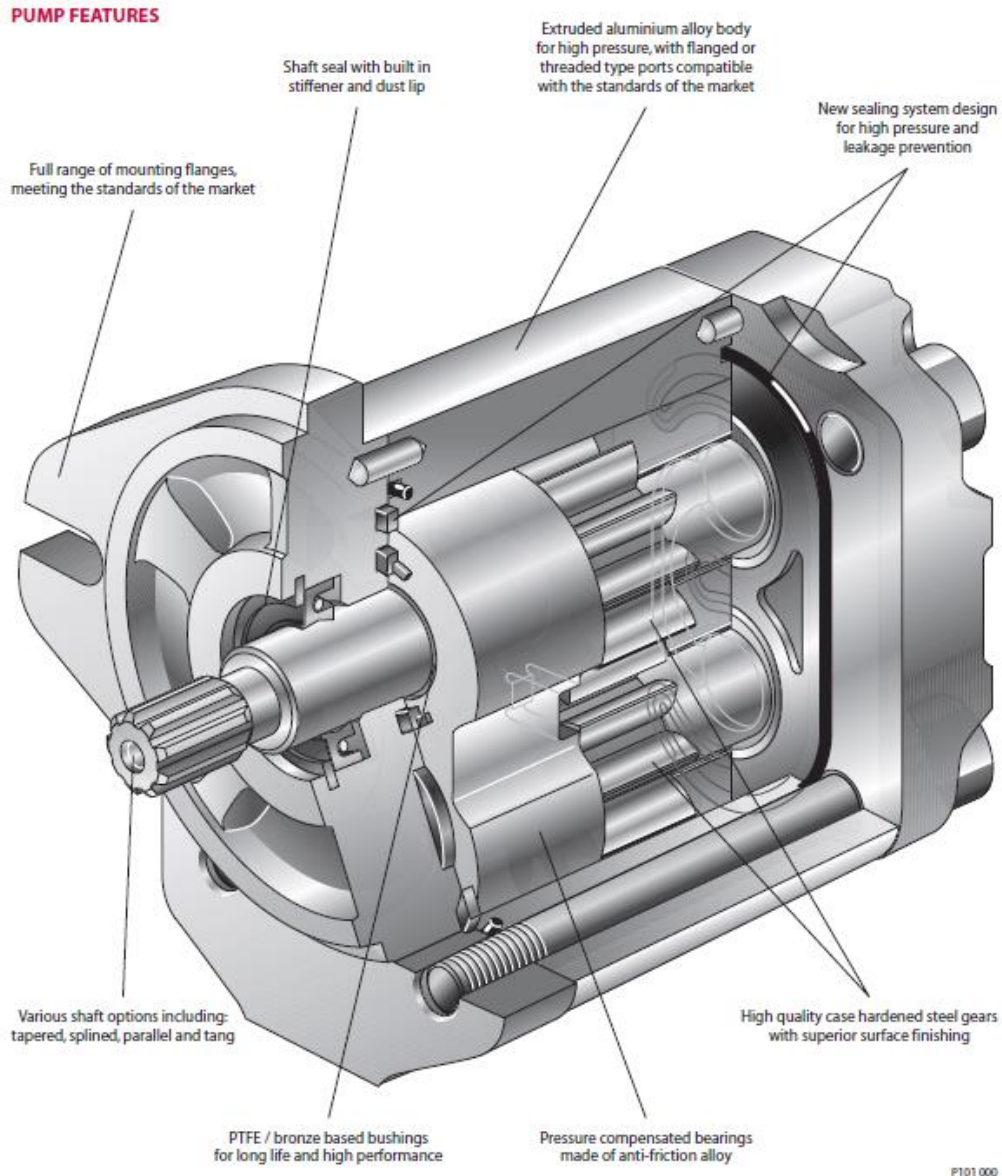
Partes constituyentes bomba de engranajes Sauer Danfoss [9]
